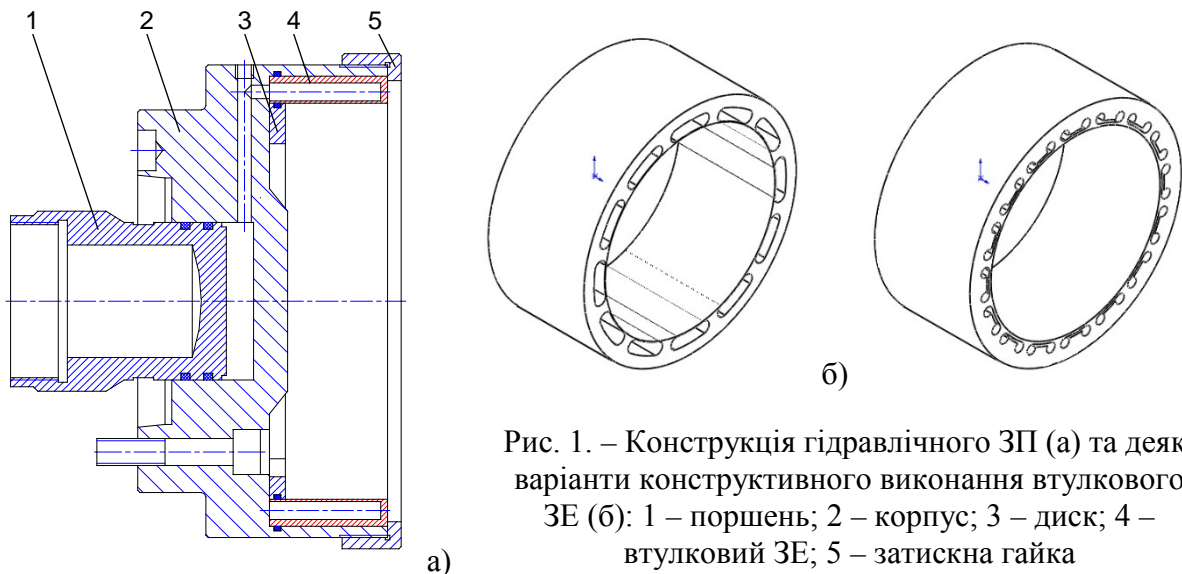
Конструкція гідравлічного ЗП (а) та деякі варіанти конструктивного виконання втулкового ЗЕ (б): 1 – поршень; 2 – корпус; 3 – диск; 4 – втулковий ЗЕ; 5 – затискна гайка
